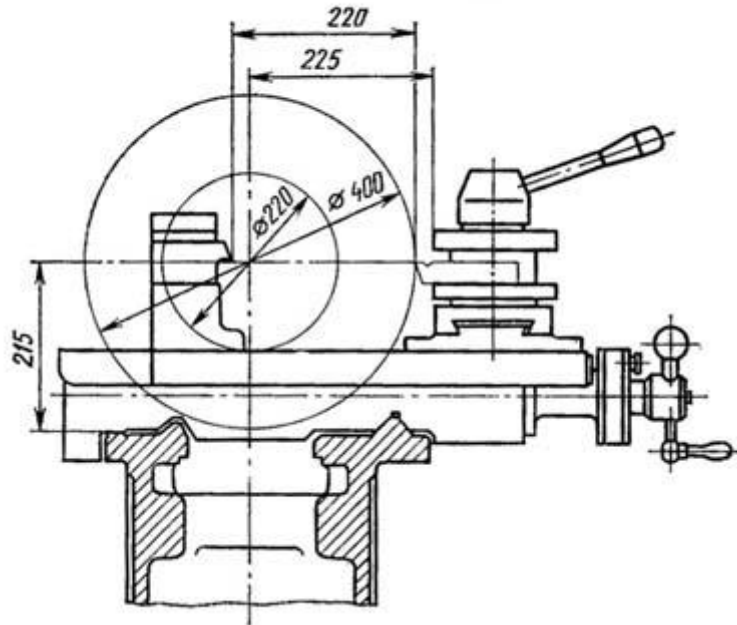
Креслення робочого простору токарного верстата 16к20
